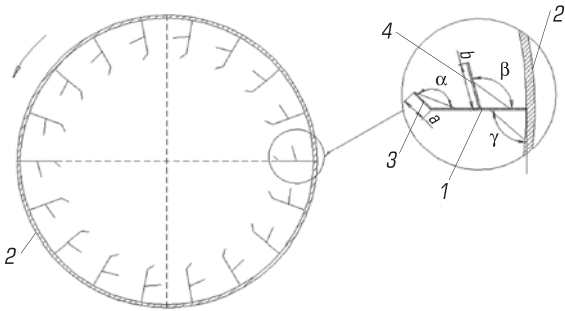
Конструкция профильной лопастной насадки с двумя лопатками барабанной сушилки [5]
